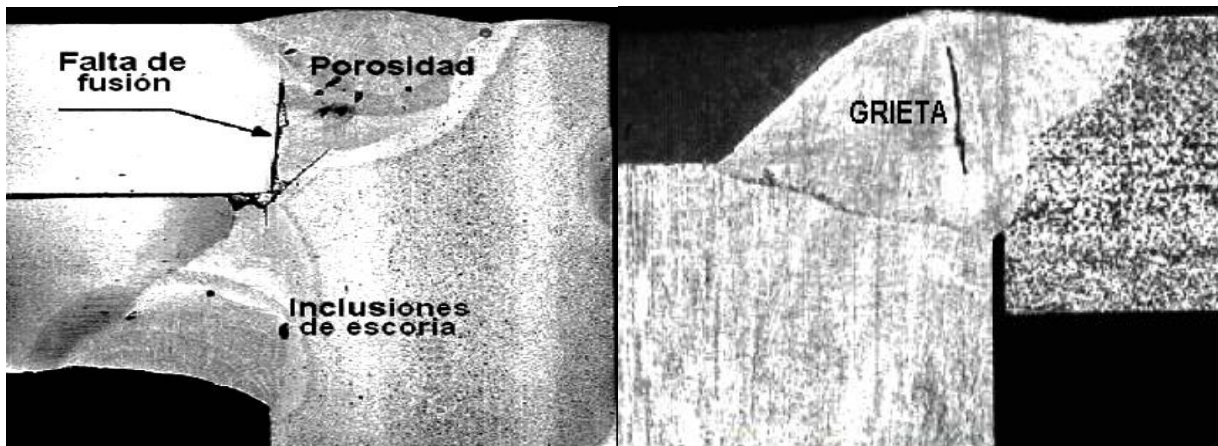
Defectos en las soldaduras (8, 18)
